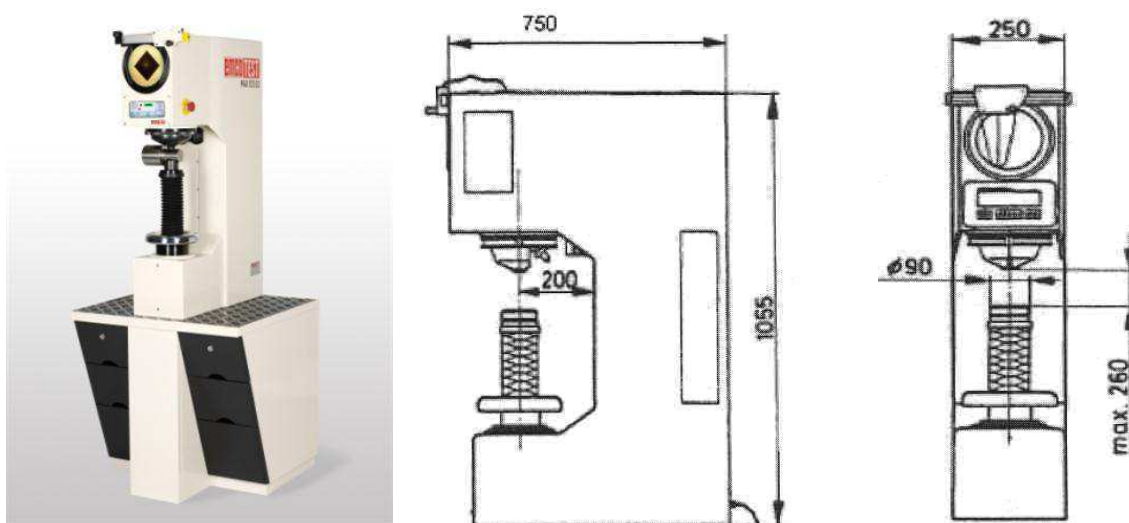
Универсальный твердомер EMCQ-TEST M4 G3
